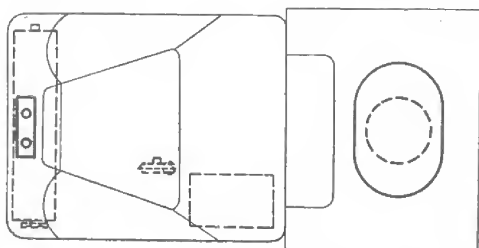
Anordnung des Gaserzeugers bei einer Zugmaschine. Gaserzeuger in der Mittelachse des Fahrzeuges
